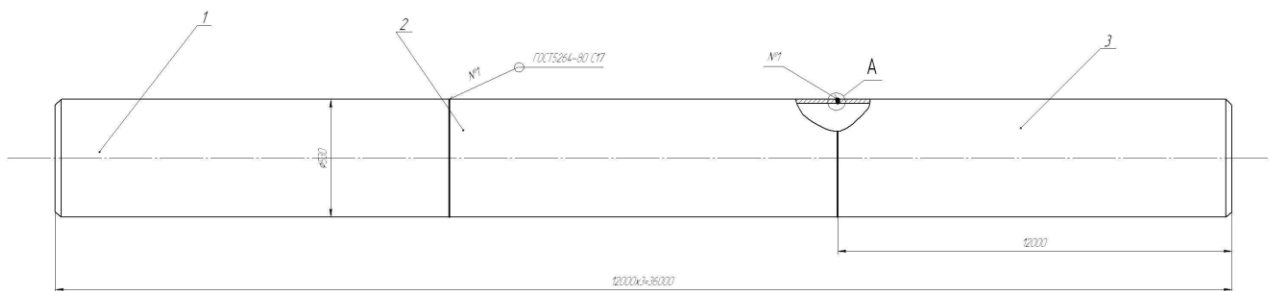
Общий вид свариваемого газопровода, вид А см. рис. 1.1.
